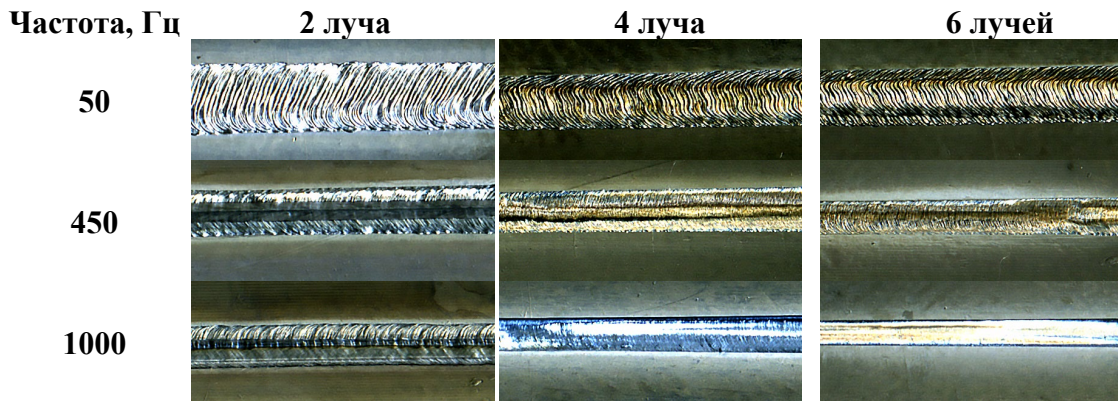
Внешний вид продольных сварных швов
